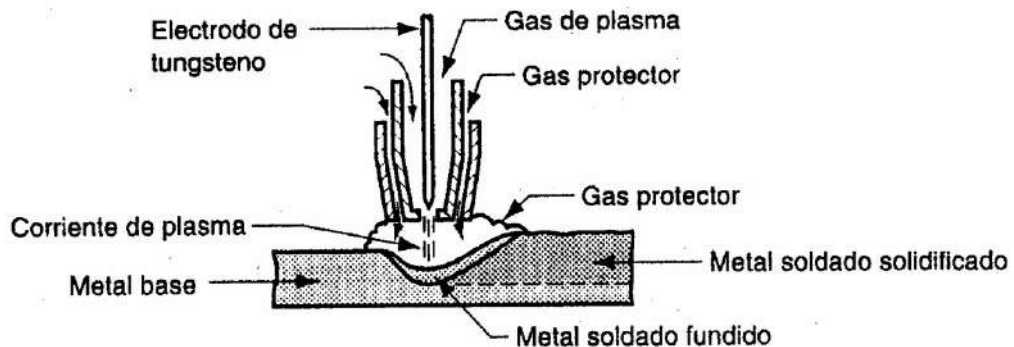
esquema de soldadura PAW, fuente: procesosmanufacturau4.weebly.com
